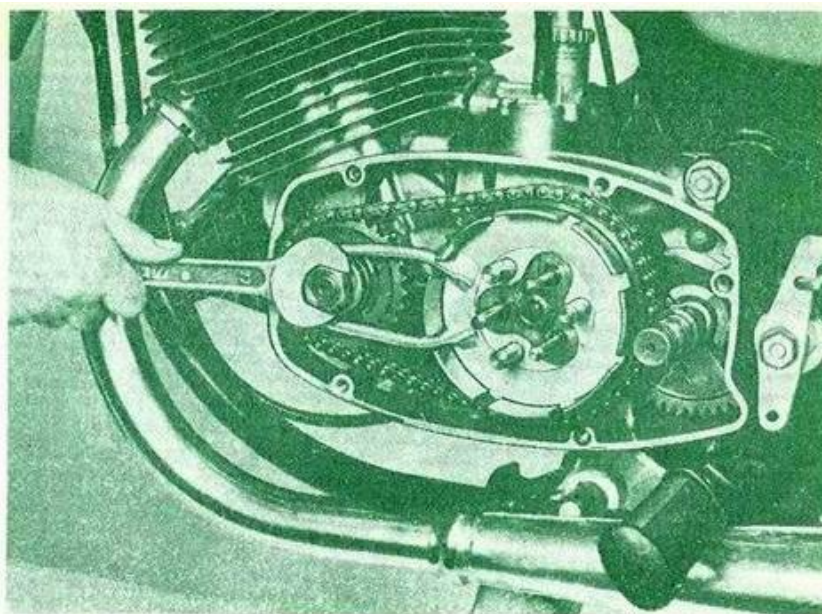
Отвертывание гайки крепления ведущей звездочки передней передачи
